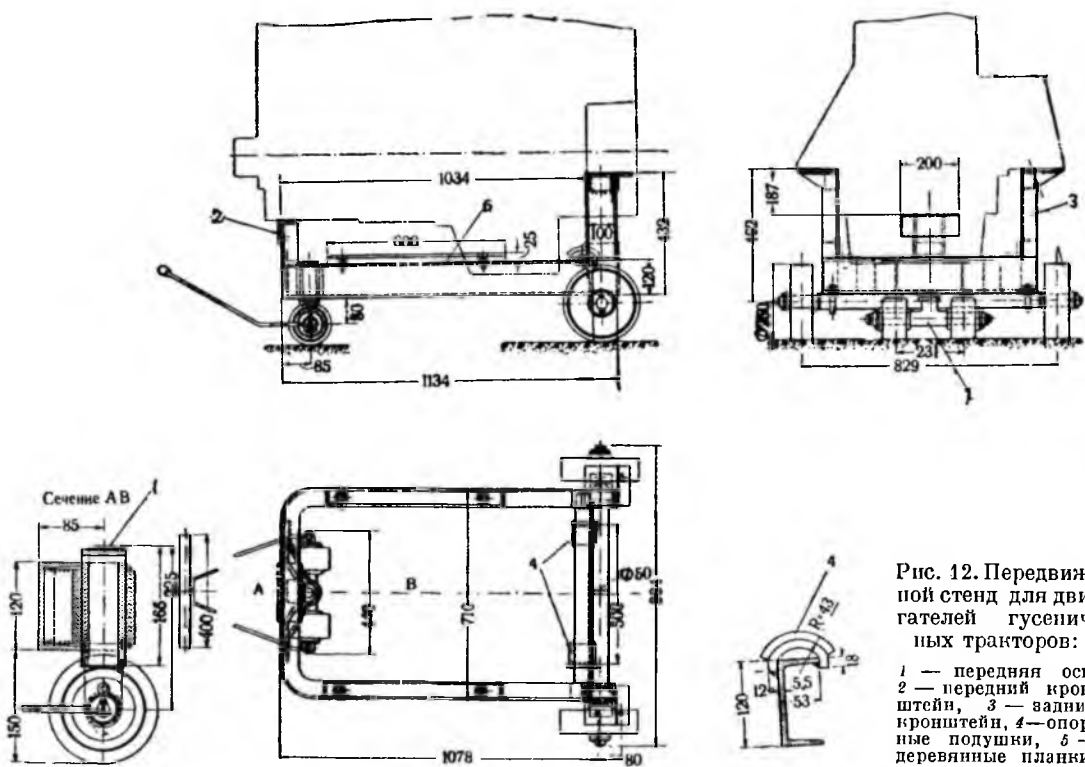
Передвижной стенд для двигателей гусеничных тракторов:
